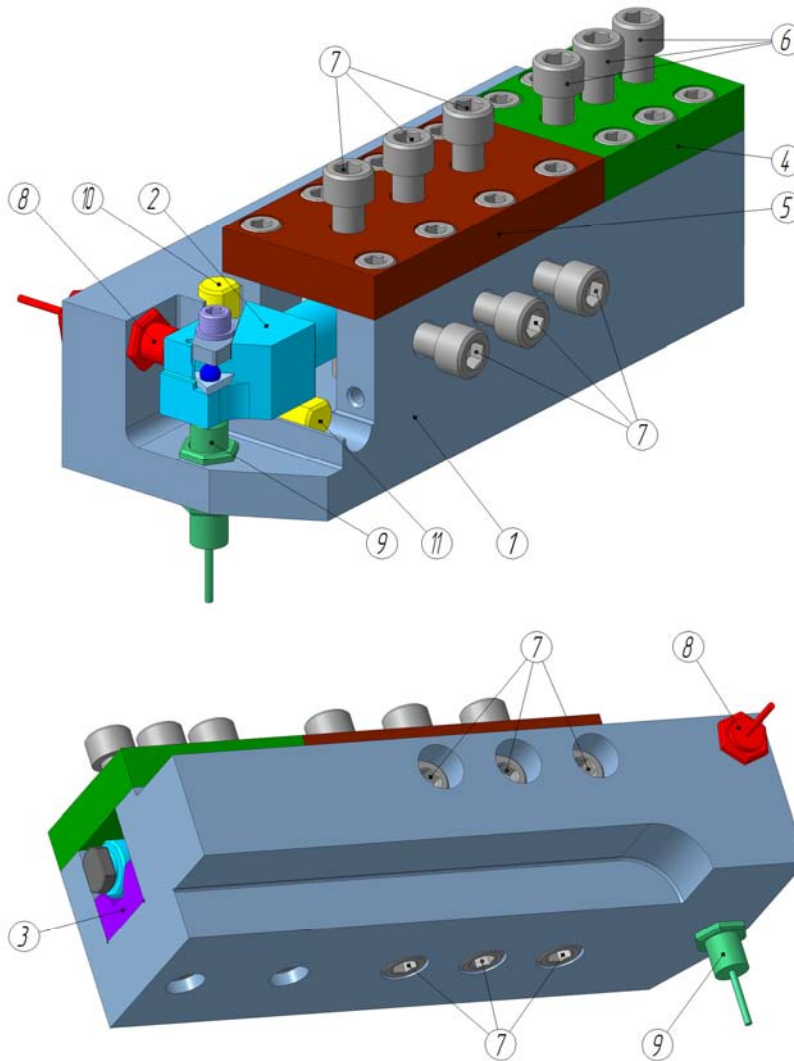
Конструкция устройства для исследования автоколебаний при точении: 1 – корпус; 2 – режущий инструмент; 3 – призма; 4 – крышка – прижим; 5 – крышка; 6 – винты фиксации режущего инструмента; 7 – винты настройки вылета режущего инструмента; 8 – датчик горизонтальных перемещений режущего инструмента, 9 – датчик вертикальных перемещений режущего инструмента; 10, 11 – бронзовые направляющие
